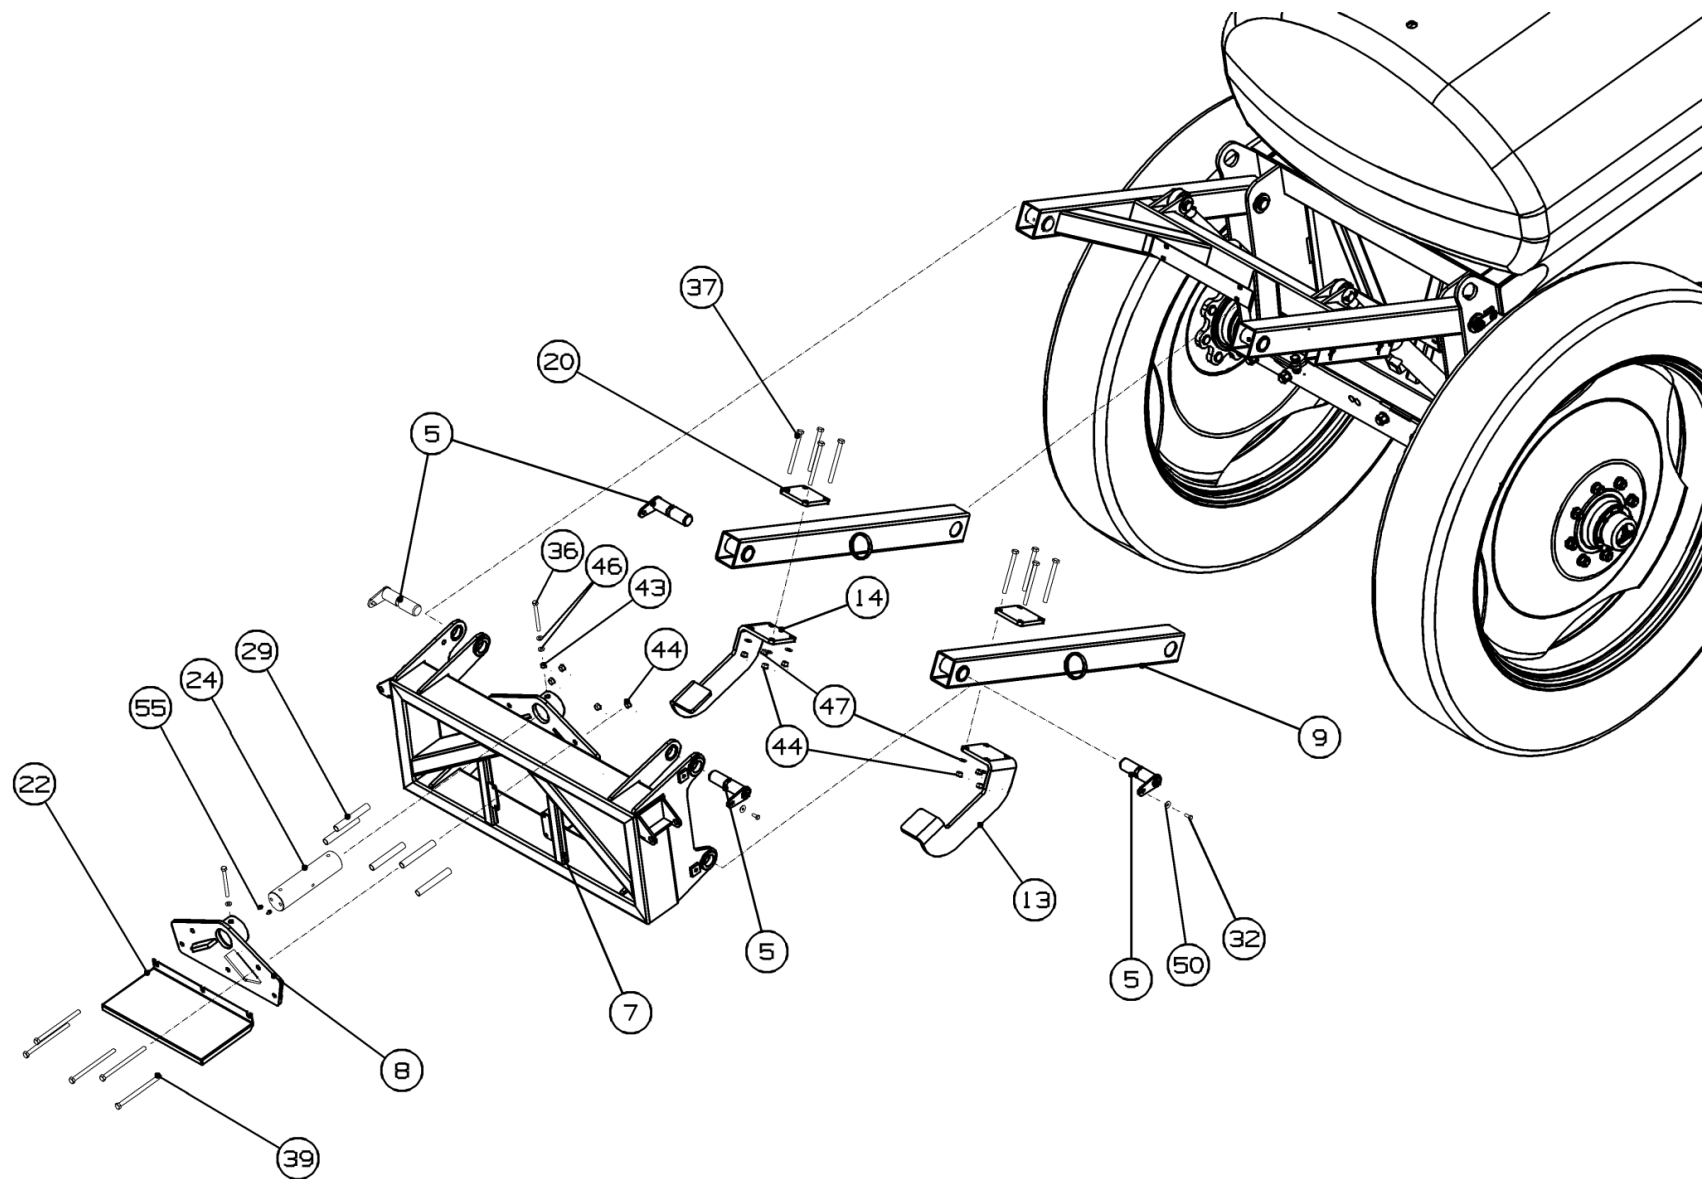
Опрыскиватель полуприцепной ОП-3200-24.01.00.000Б (вид сзади)
